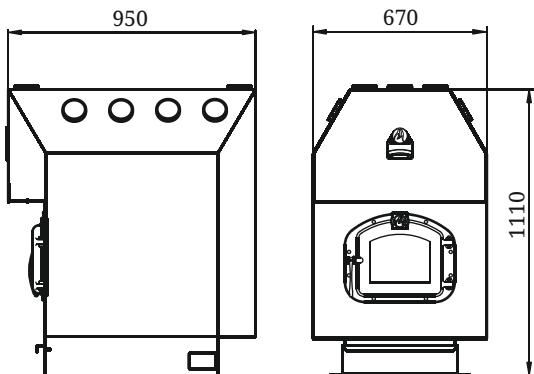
Габаритные размеры печи «Профессор» с выходом трубы вверх
